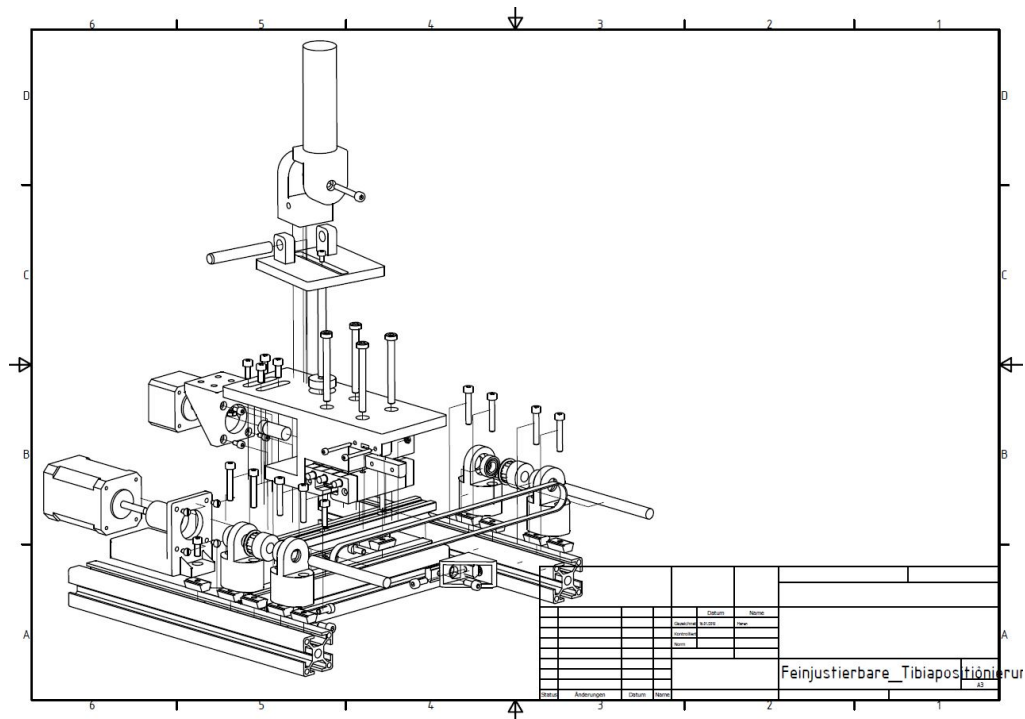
Explosionszeichnung des Gerätes zur Justierung der künstlichen Tibia
